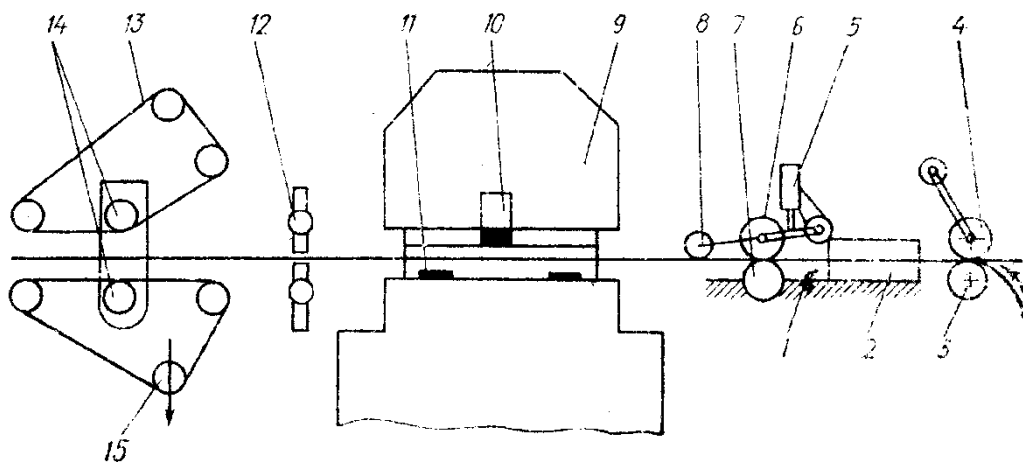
Схема подачи картонного полотна в штанцевальный аппарат и механизма выдачи листов с высечками:
